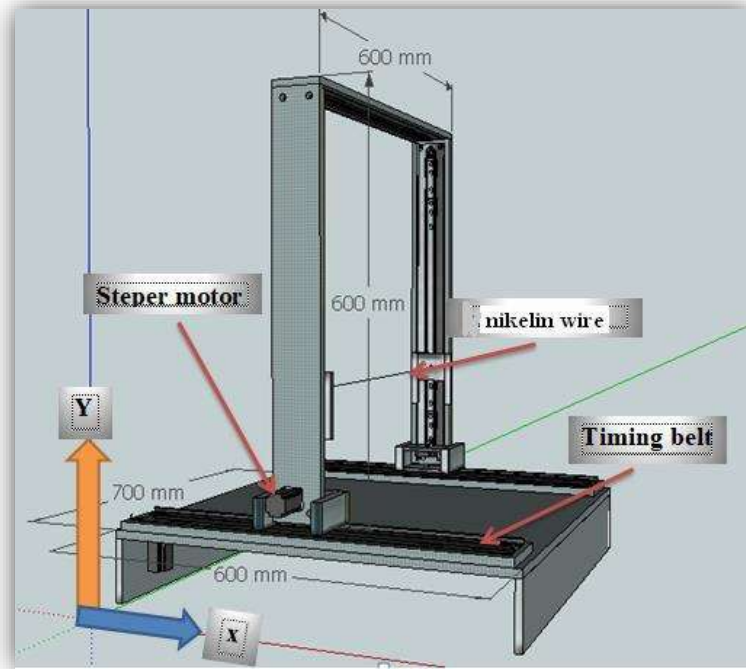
Les dimensions de la machine CNC à chaud [22]
